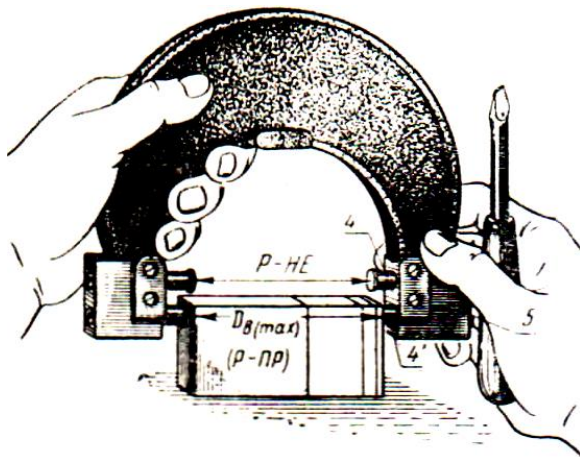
Положение скобы при установке проходного размера по блоку концевых мер
